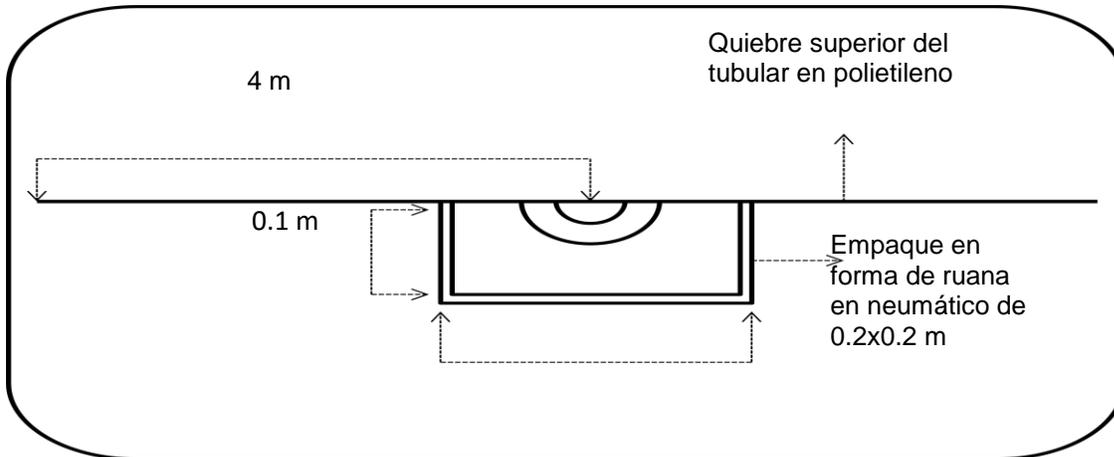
Detalle de la instalación de empaque para salida del biogás.
